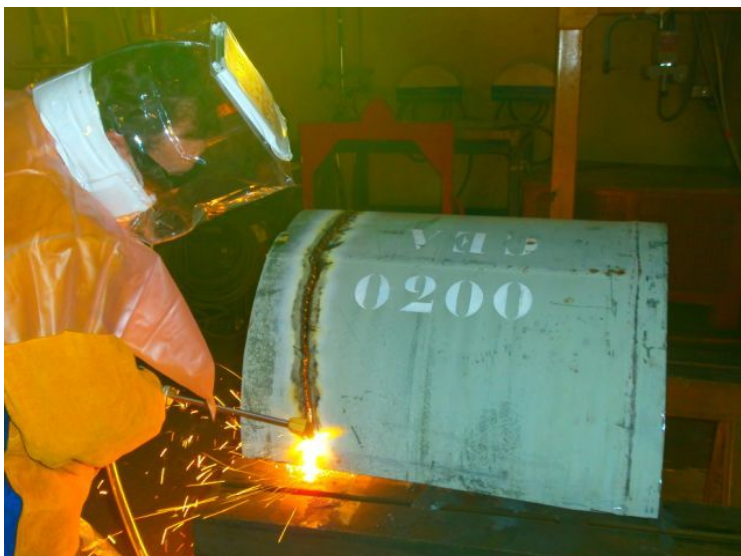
Découpe à l'aide d'une torche plasma (par point chaud)
